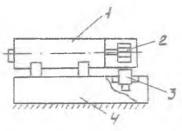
Схема установки даттика ДЧВ-250 при проверке форми и уровня выходного сигнала: І - электродвигатель: 2 — индуктор; 3 — цатик ДЧВ-2500; 4 — станина
